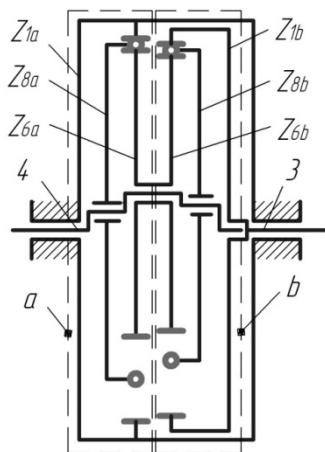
Кинематическая схема планетарного механизма (с условными опорами сепараторов)
